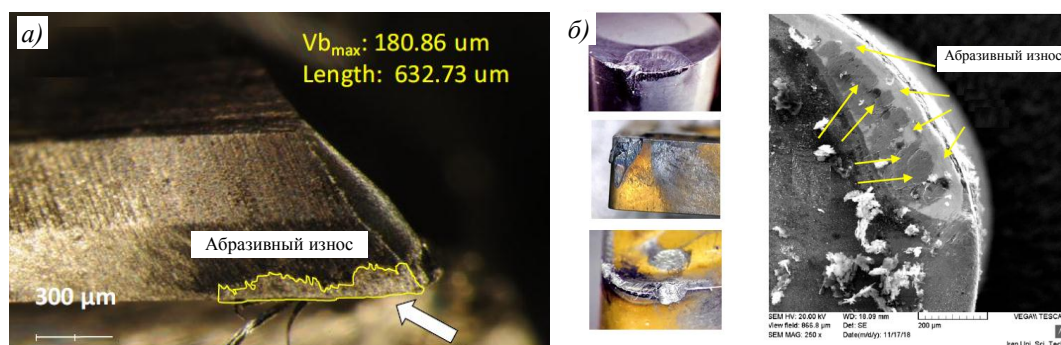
Абразивный износ поверхности фрезы (а) и токарного инструмента (б)
